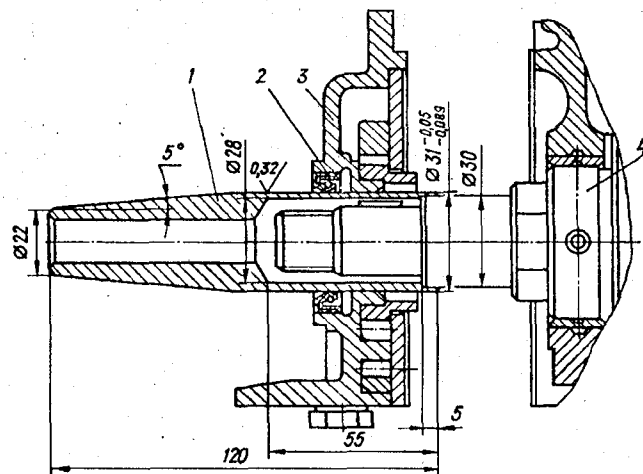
Установка масляного насоса на носок коленчатого вала: 1 — оправка; 2 — манжета; 3 — масляный насос; 4 — коленчатый вал
